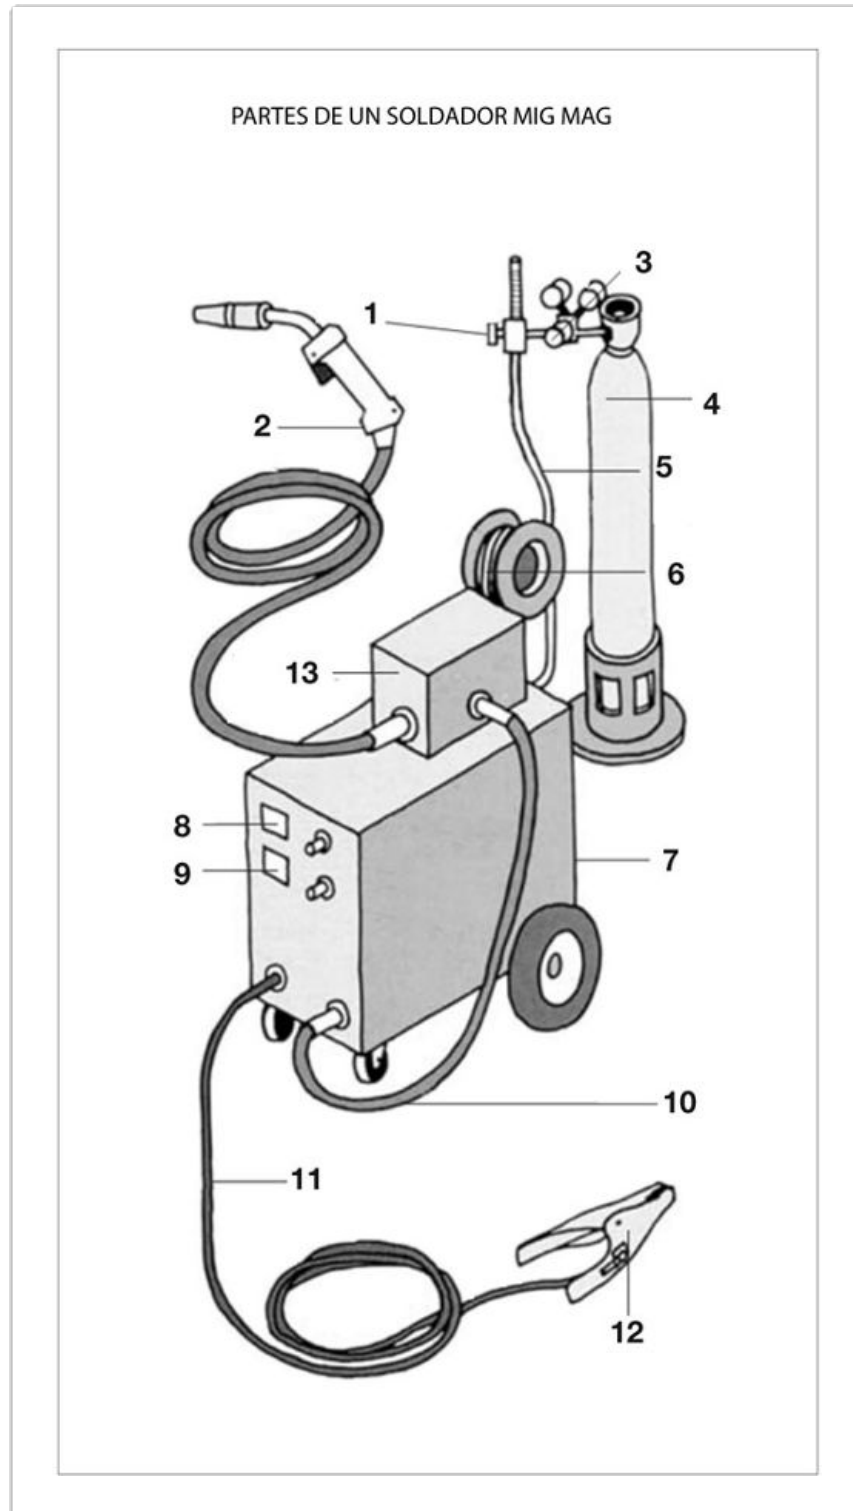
Partes de una Máquina Soldadora.
